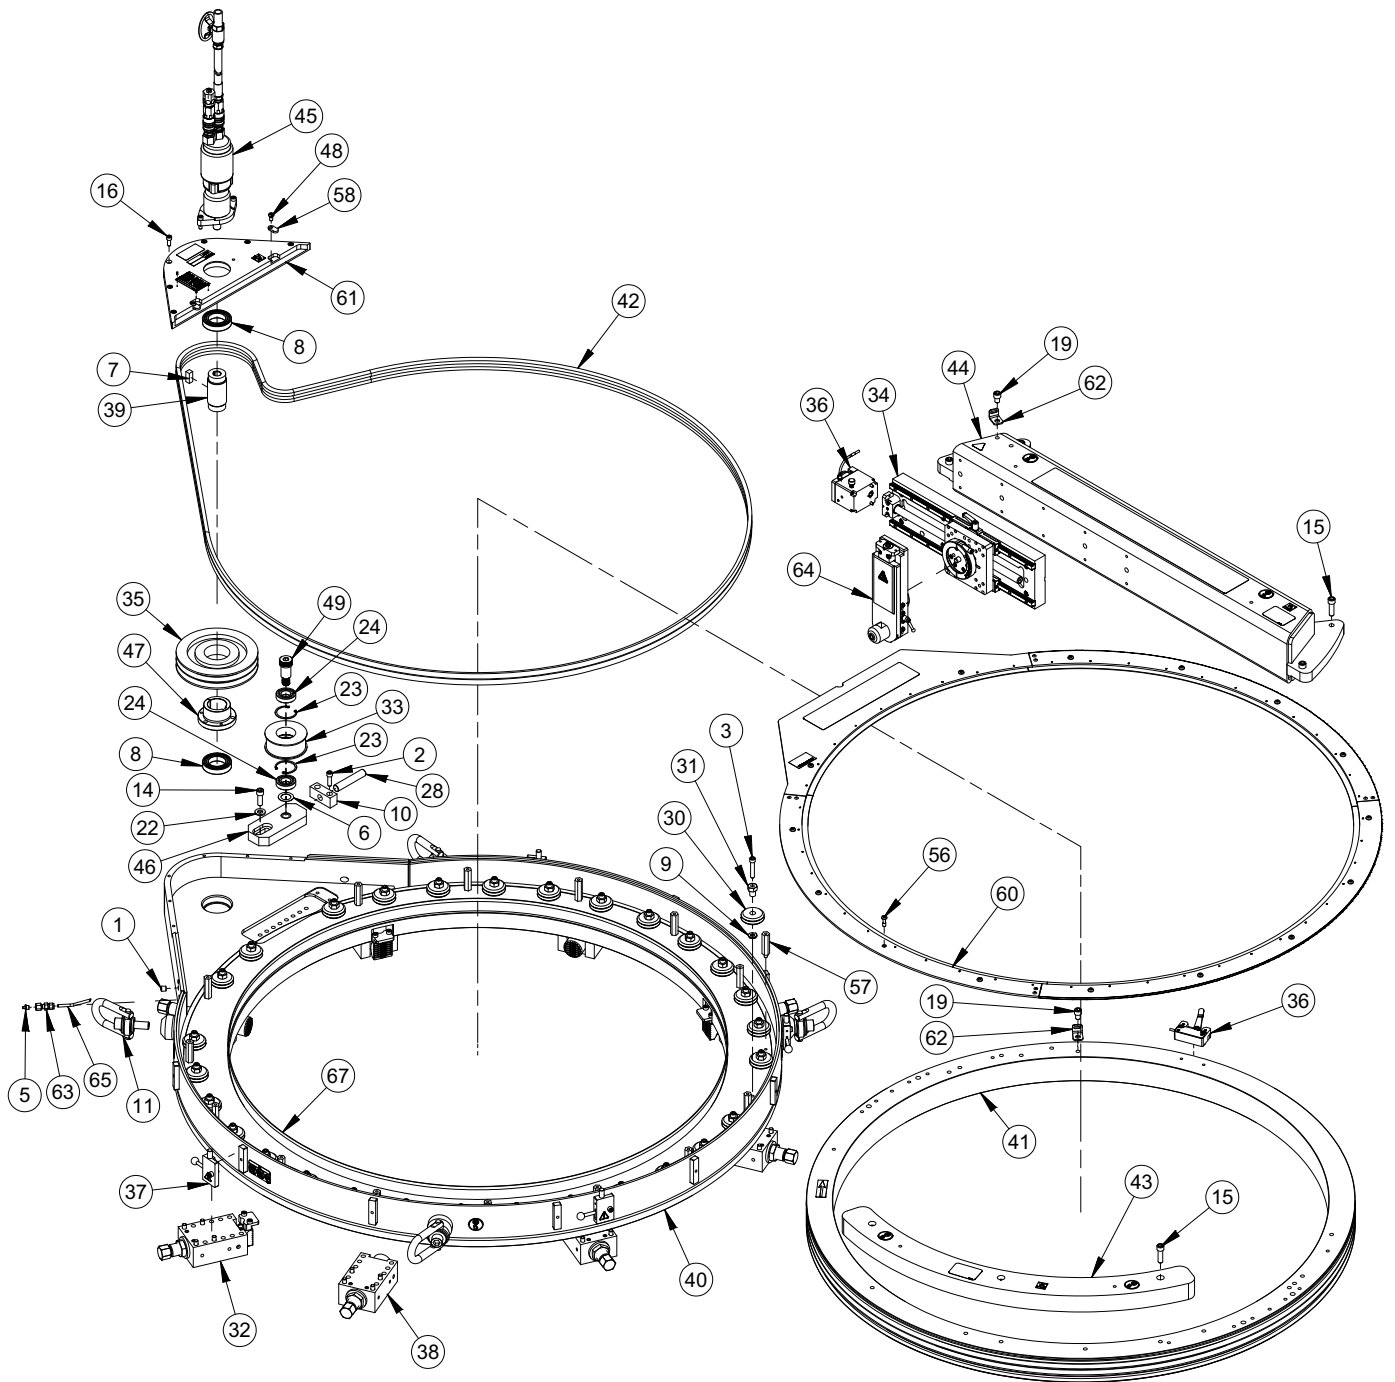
CONJUNTO DEL ODF50 SPEED FACER (N/P 86980)
